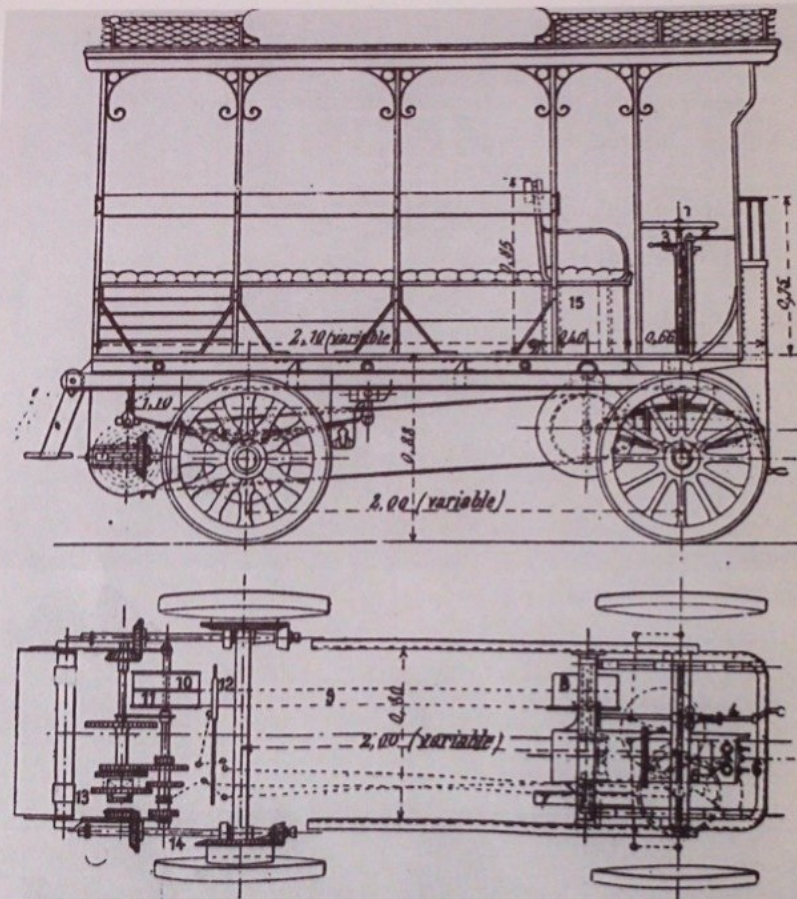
Élévation longitudinale et vue en plan du break de Dietrich.
